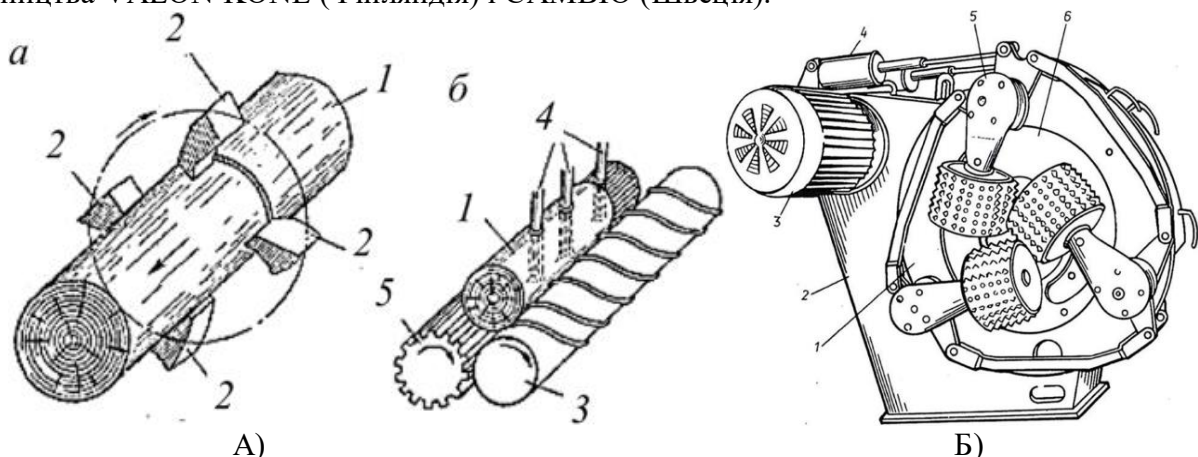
Робота окорювальних верстатів: А) Роторних та гідравлічно-пневматичних; Б) Загальний вигляд роторного верстата Cambio 70-65AA:.
